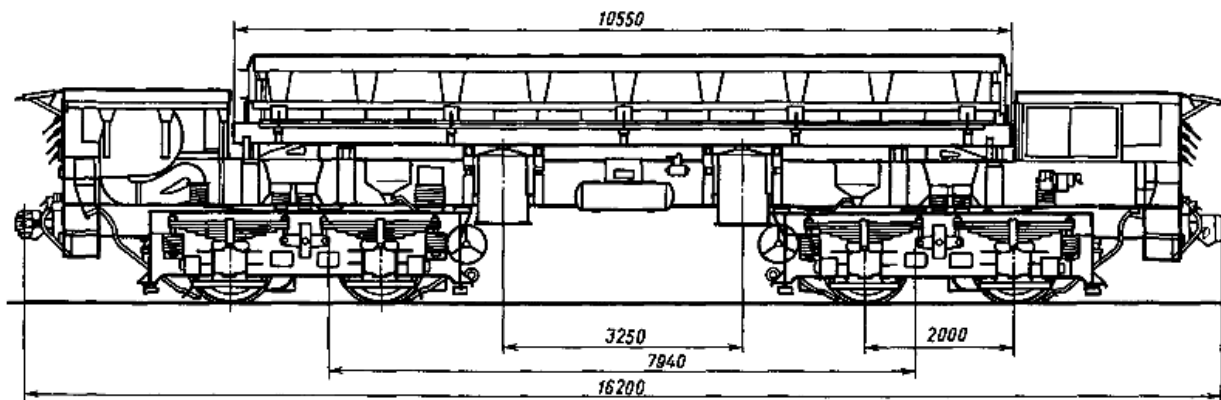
Основные размеры моторного думпкара тягового агрегата серии ЕЛ10 с № 011
